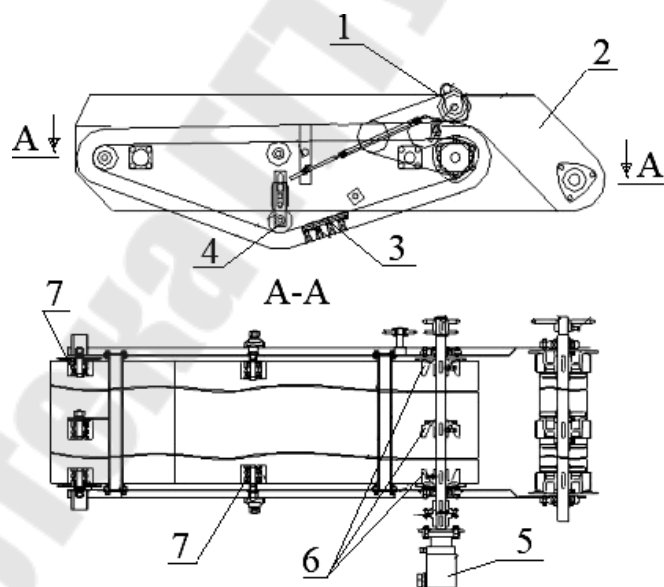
Наклонная горка: – валец отбойный; 2 – рама; 3 – транспортер отделительный; 4 – устройство натяжное; 5 – гидромотор; 6 – колеса приводные; 7 – ролики поддерживающие
